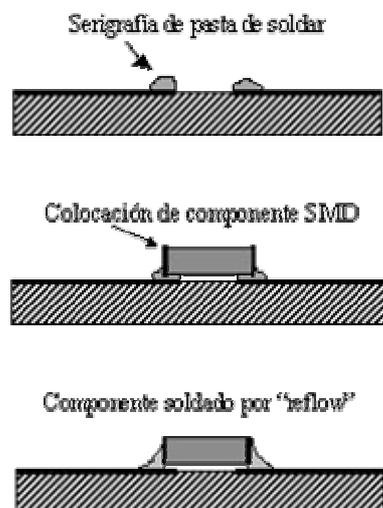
SMT empleando la técnica de soldadura por “reflow”
